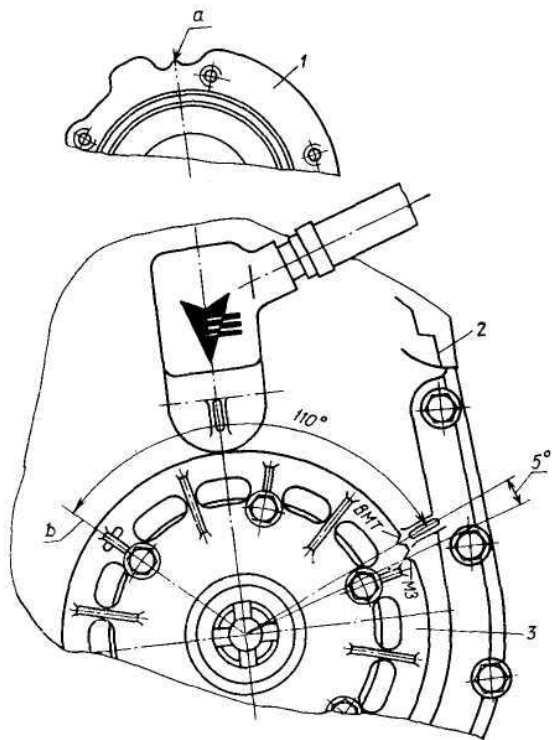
Установочные метки на крышках центробежного маслоочистителя и распределительных шестерён:
